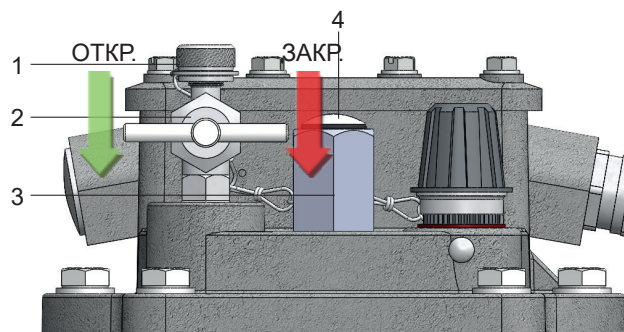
Крышка газового реле с маслозаливным патрубком (код 29D)
